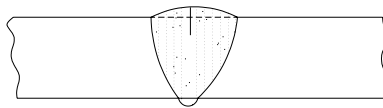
Penetração excessiva de metal de solda em junta de topo.
